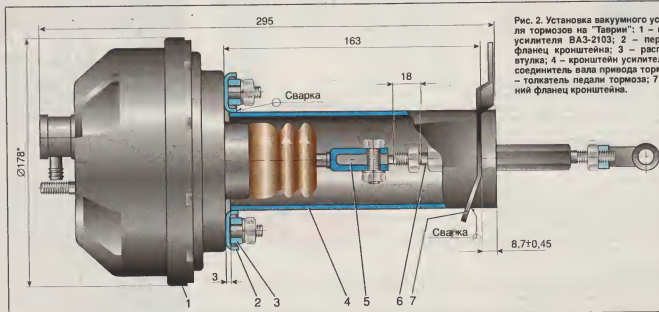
Установка вакуумного усилителя тормозов на "Таврий": 1 — корпус усилителя ВАЗ-2103; 2 — передний фланец кронштейна; 3 — распорная втулка; 4 — кронштейн усилителя; 5 — соединитель вала привода тормоза; 6 — толкатель педали тормоза; 7 — задний фланец кронштейна.
